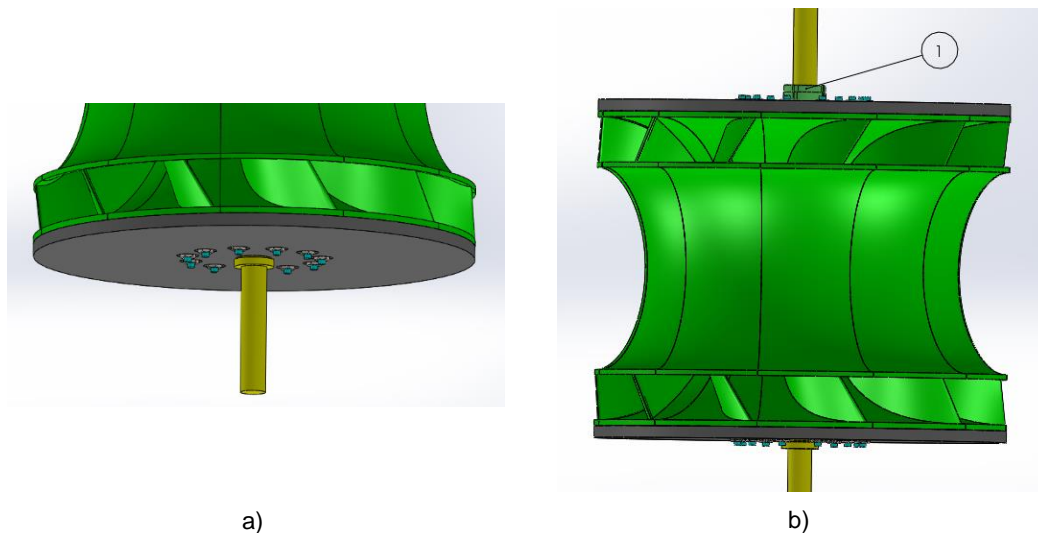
Conceito 3 para fixação do rotor ao veio: a) Pormenor do ressalto no veio; b) Representação global do subconjunto rotor e veio da turbina
